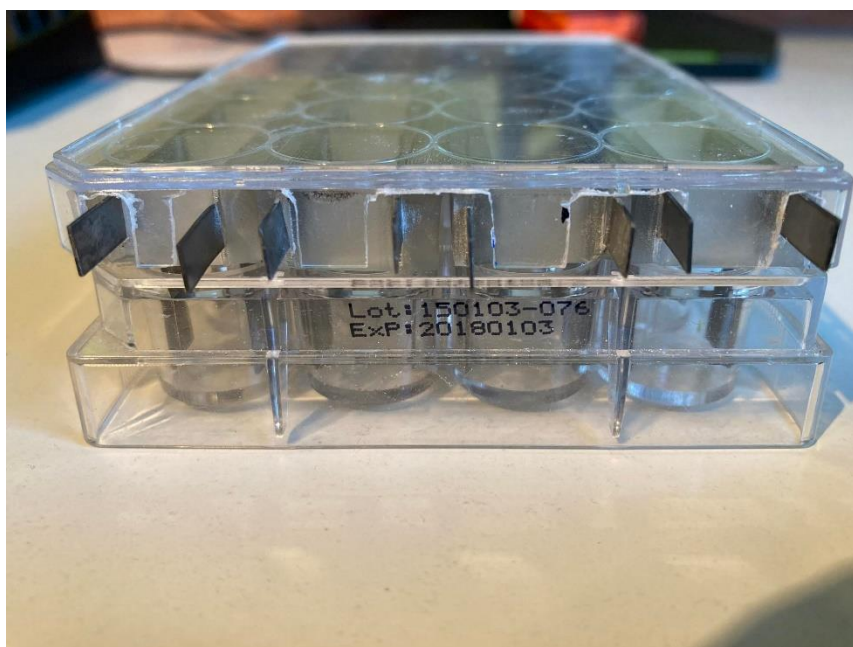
Proces frézování (Zdroj: autor) Obr. 22 Výsledek frézování (Zdroj: autor)
